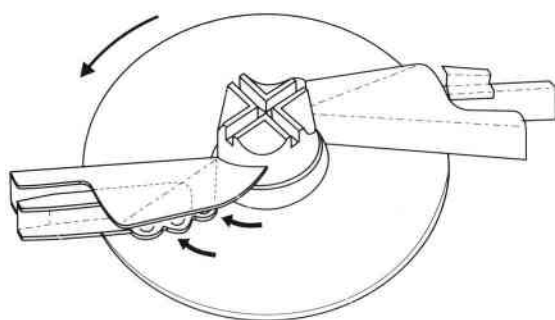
Principe du réglage du point de chute par déplacement de l'ensemble disque-moteur hydraulique
